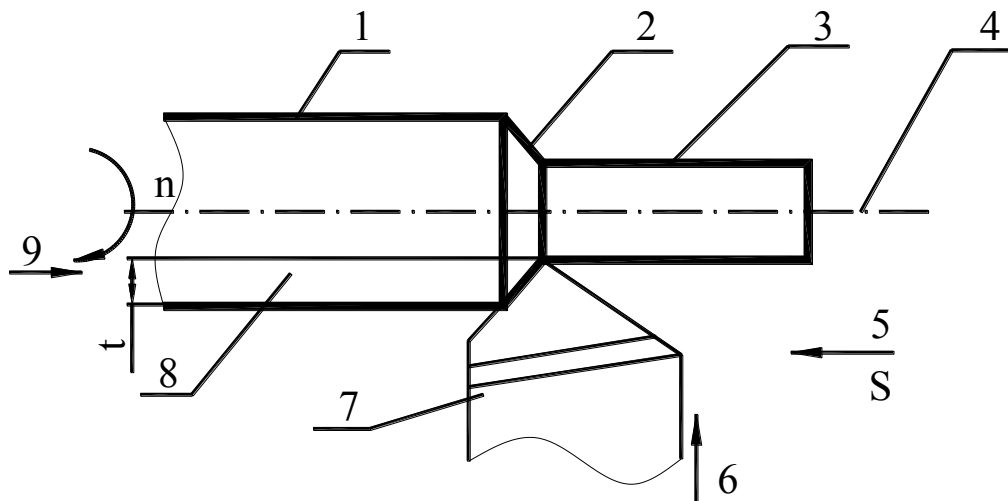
Основні поверхні заготовки і основні рухи, що здійснюють процес різання: 1 - оброблювана поверхня; 2 - поверхня різання; 3 - оброблена поверхня; 4 - вісь обертання заготовки; 5 - поздовжня подача; 6 - поперечна подача; 7 -різець; 8 - заготовка; 9 - головний (обертальний) рух; t - глибина різання
